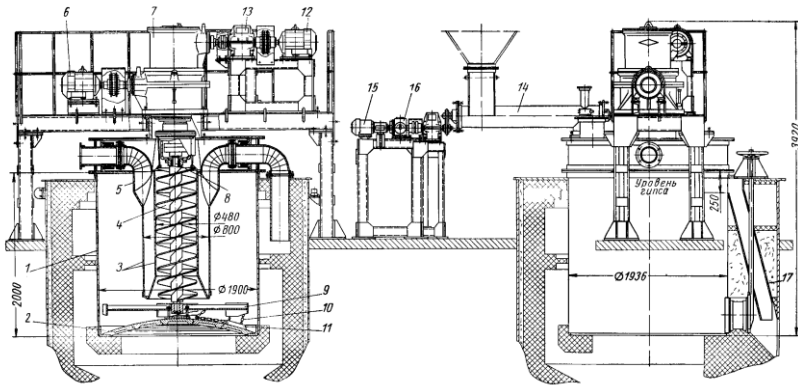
Загальний вигляд гіпсоварочного котла безпервної дії: 1 – корпус, 2 – днище, 3 – стакан, 4 – шнек, 5 – топочні патрубки, 6 – електродвигун приводу обертання шнека, 7 – конічний редуктор, 8 – вал мішалки, 9 – лопать мішалки, 10 – ланцюги, 11 – косинець, 12 – електродвигун приводу обертання мішалки, 13 – циліндричний редуктор, 14 – гвинтовий живильник, 15 – електродвигун приводу руху живильника, 16 – ланцюговий варіатор, 17 – вивантажувальна напрямна воронка, 18 – рівень гіпсу в котлі.
